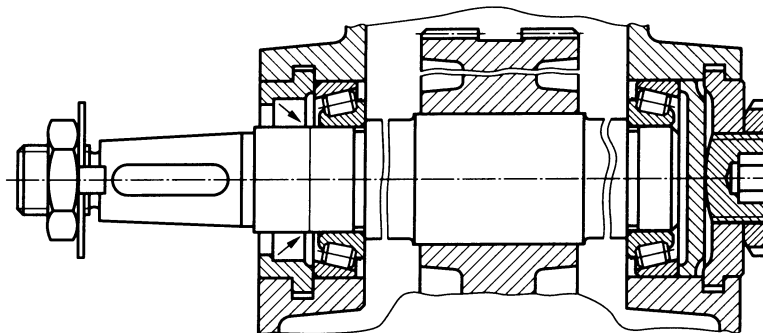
Выходной вал шевронного редуктора (мотор-редуктора)
